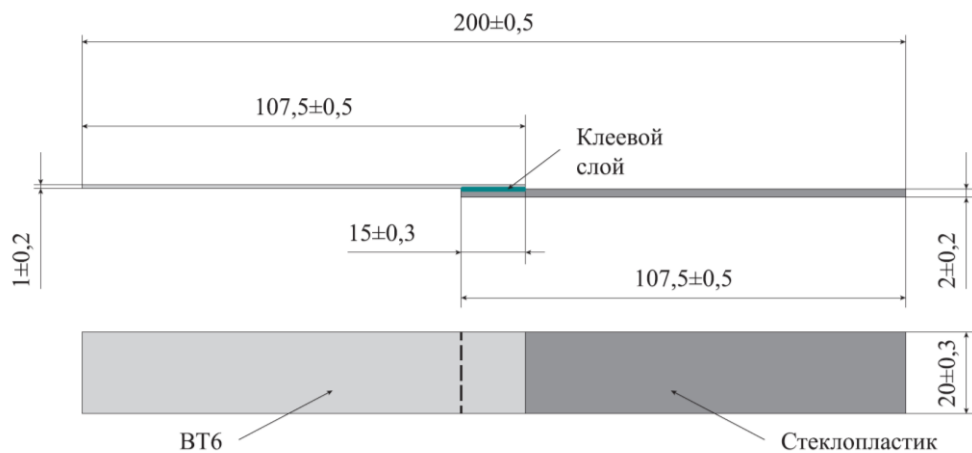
Схема образца для испытания клеевого соединения элементов из стеклопластика и титанового сплава
